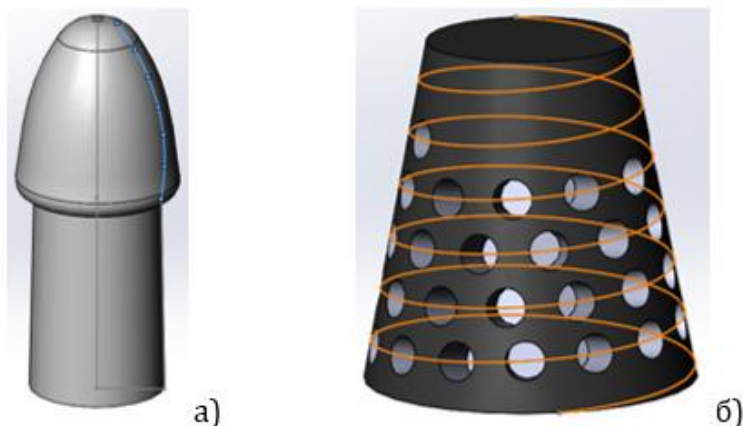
Особливості конструкції зубчатих конусних коліс: а – утворення робочої поверхні зубця; б – схема розміщення отворів для встановлення зубців
